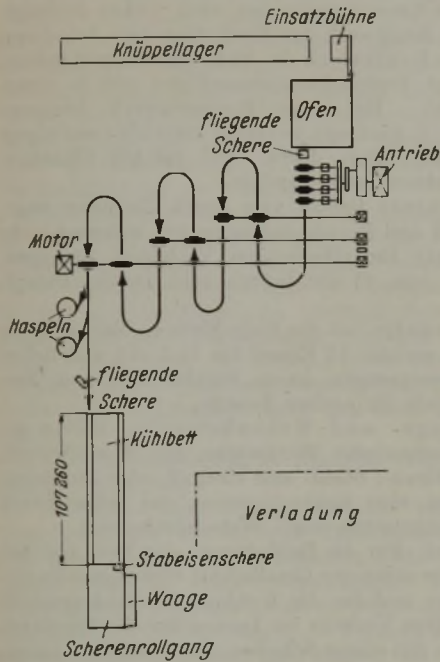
Lageplan der 254er Stabstahlstraße (Nr. 16).
